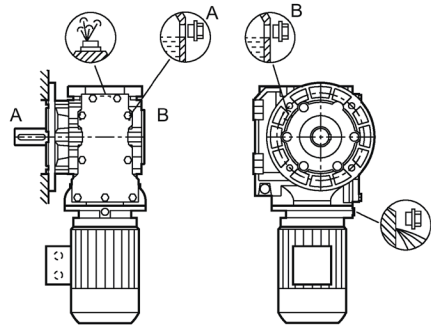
Einbautagen für Stirnradschneckengetriebe CF Flanschausführung und CAZ mit Gehäuseflansch, Baugröße 29
